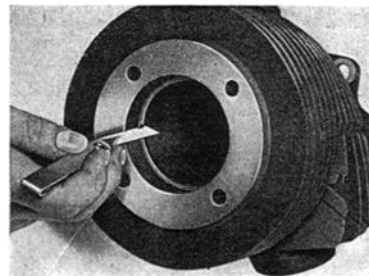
Messen des Kolbenring-Stoßmaßes mittels Fühllehre
